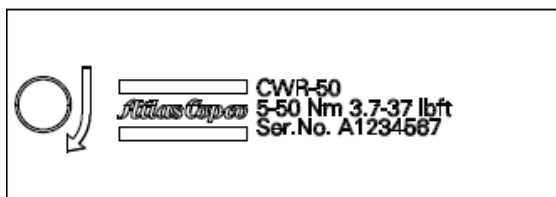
Общий вид типовой маркировки ключей серий CWR
